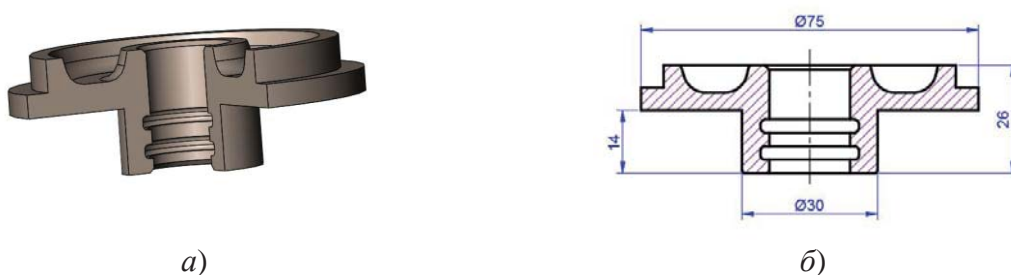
Деталь с фланцем типа «вкладыш»: 3D – представление (а) и основные размеры (б)
